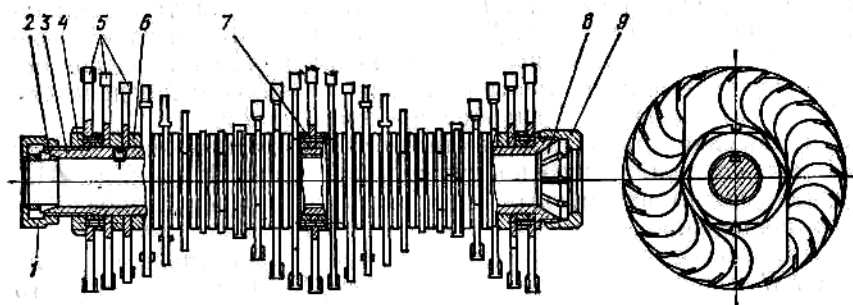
Фрезерная головка одностороннего шипорезного станка для ящичных прямых шипов:
